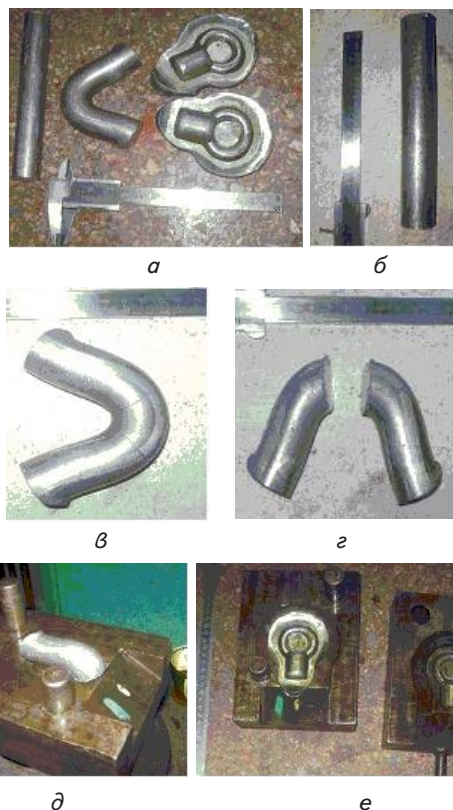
Штамповка поковки «рым-болт» по усовершенствованной технологии: а – последовательность переходов; б – исходная заготовка на две поковки (Ø26×152 мм); в – профилированная заготовка; г – заготовка после разделения; д – укладка заготовки в штамп; е – отштампованная поковка с облоем на штампе
